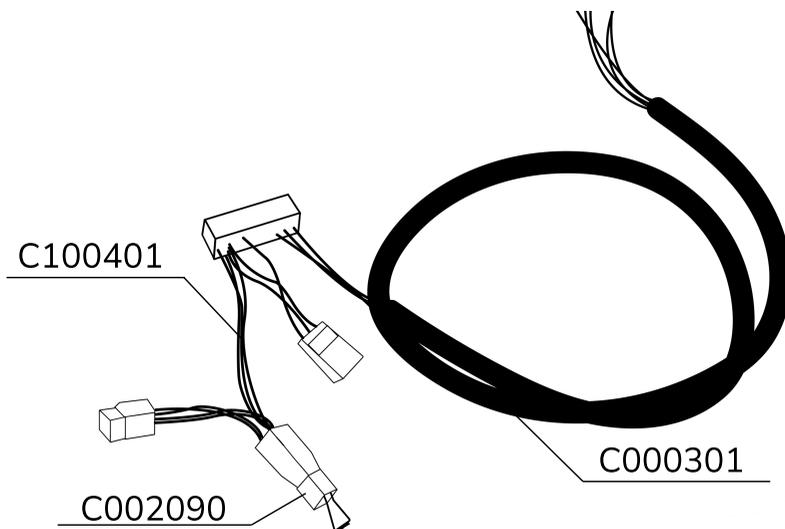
Cavo KeyDN - Macchina: C000301 + C100401 + C002090
